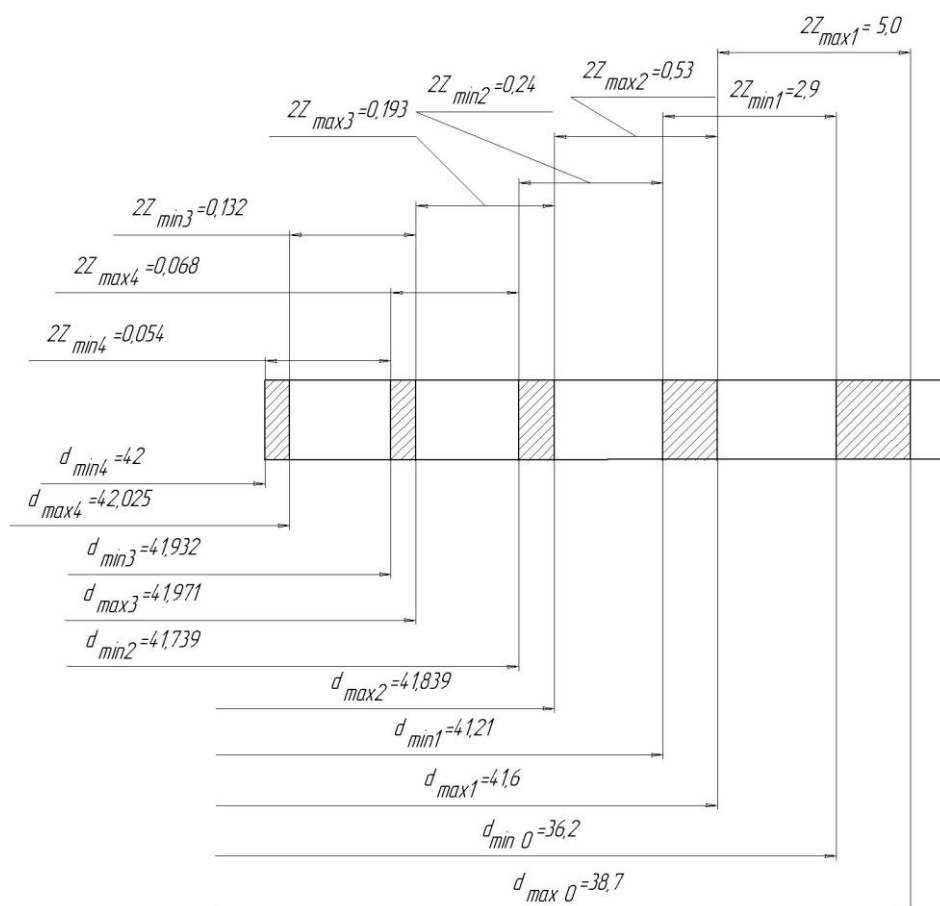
Припуски с размерами для отверстия корпуса
